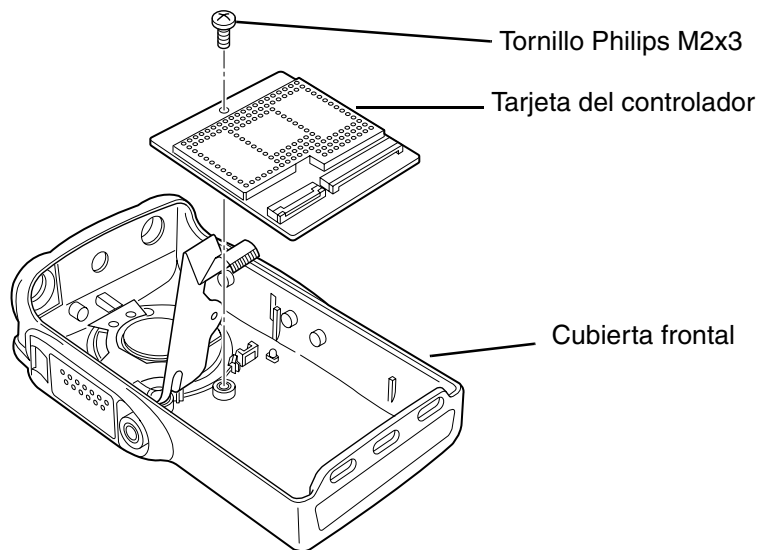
Retiro de la tarjeta del controlador de la cubierta frontal
